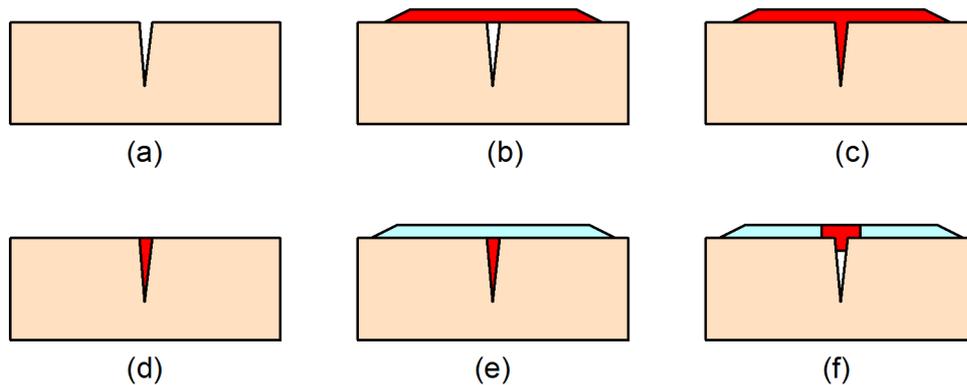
Princípios básicos da inspeção com líquidos penetrantes: (a) peça com trinca superficial, (b) aplicação do líquido penetrante, (c) penetração, (d) remoção do excesso de líquido, (e) aplicação do revelador e (f) formação da indicação da trinca.
